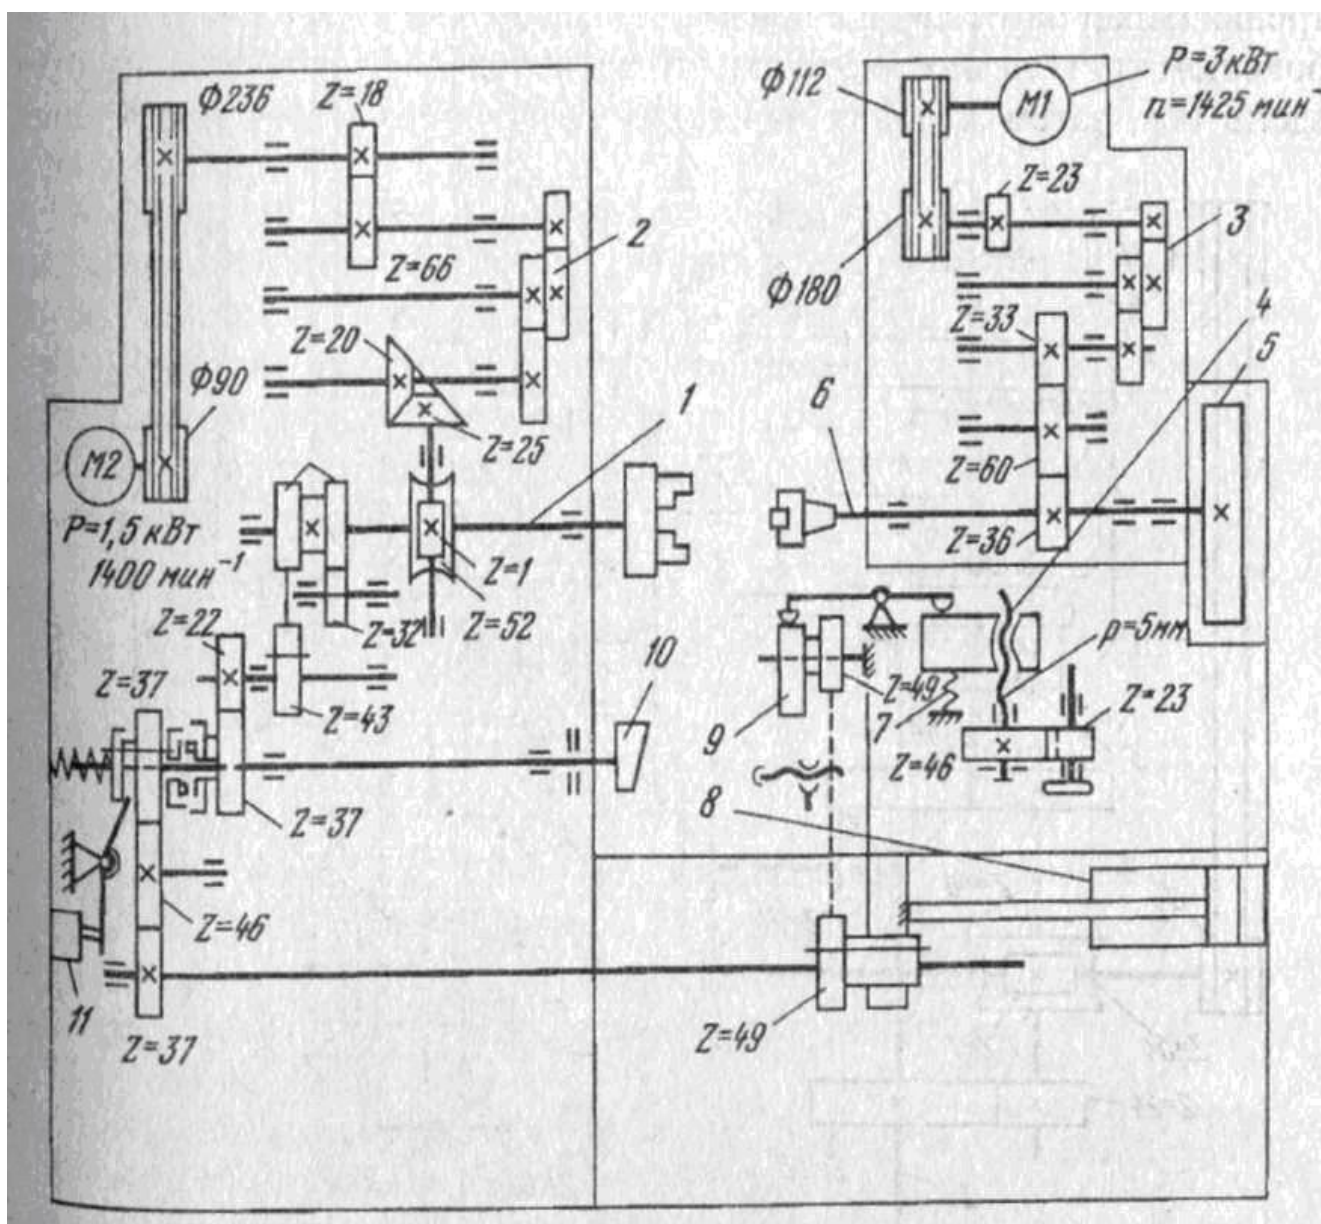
Кинематическая схема резьбофрезерного полуавтомата модели 5Д63.
